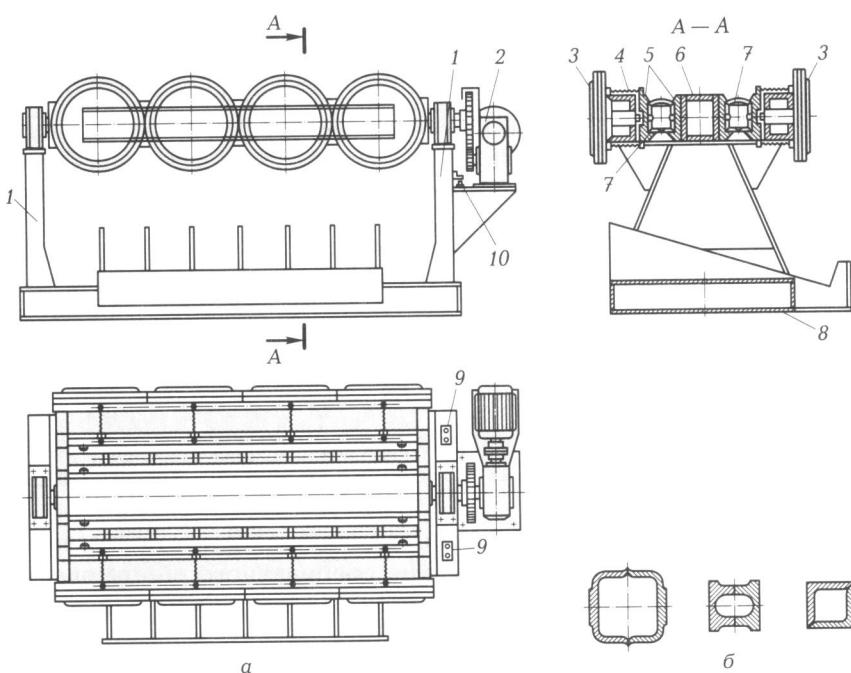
Двухпозиционный поворотный кондуктор для сборки и сварки коротких коробчатых балок:
